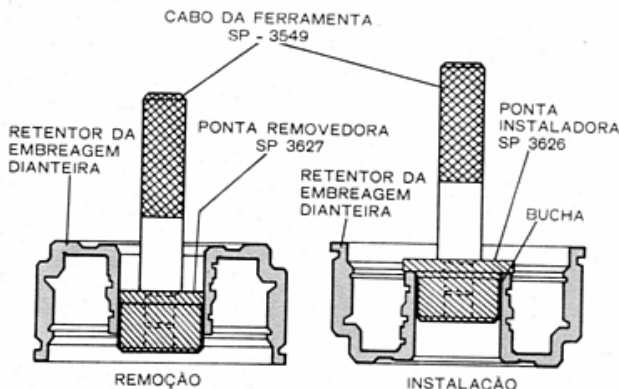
Substituição da bucha do retentor da embreagem dianteira
